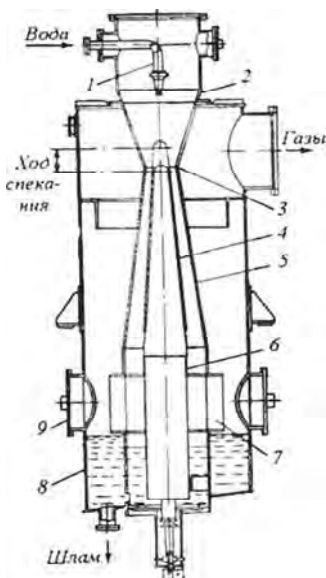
Скруббер Вентури типа СВ с коническим обтекателем: 1 – форсунка; 2 – конфузор; 3 – горловина; 4 – регулирующий конический обтекатель; 5 – диффузор; 6 – направляющий патрубок; 7 – центробежный завихритель; 8 – корпус каплеуловителя; 9 – люк
